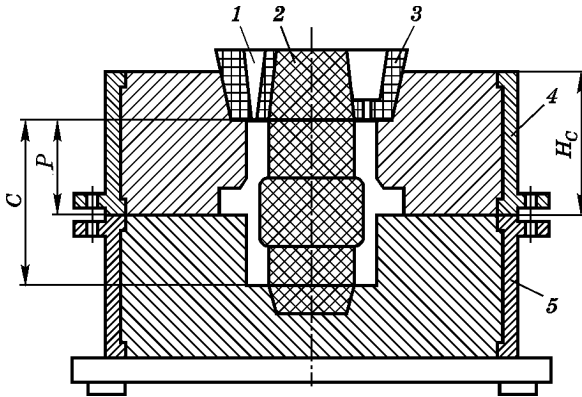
Схема ливникової форми в розрізі для визначення середнього ефективного напору  $H_n$ :
